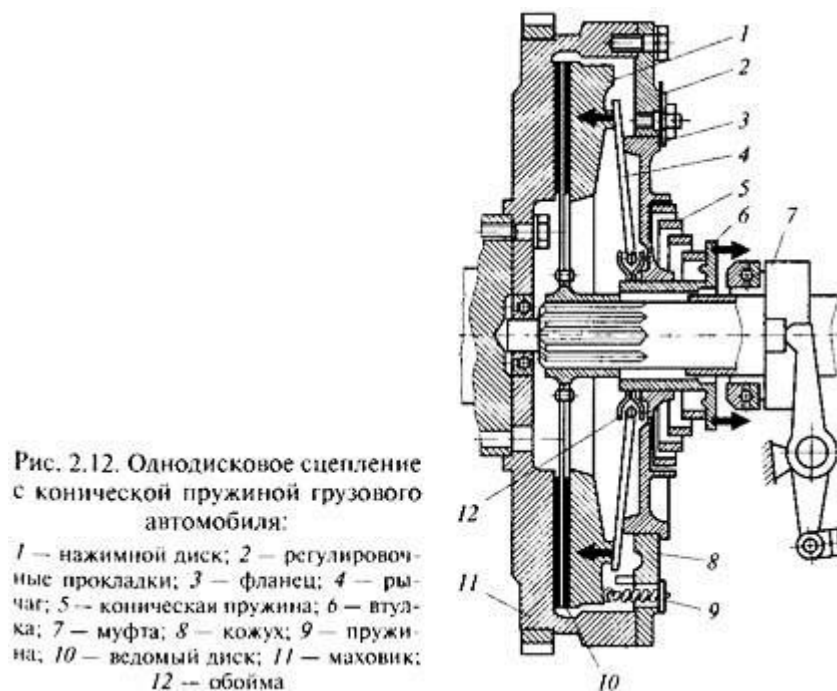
Однодисковое сцепление с конической пружиной грузового автомобиля: 1 - нажимной диск; 2 регулировочные прокладки; 3 — фланец; 4 - рычаг, 5— коническая пружина; 6 — втулка; 7 — муфта; 8 кожух; 9 - пружина; 10— ведомый диск; 11— маховик; 12 — обойма
